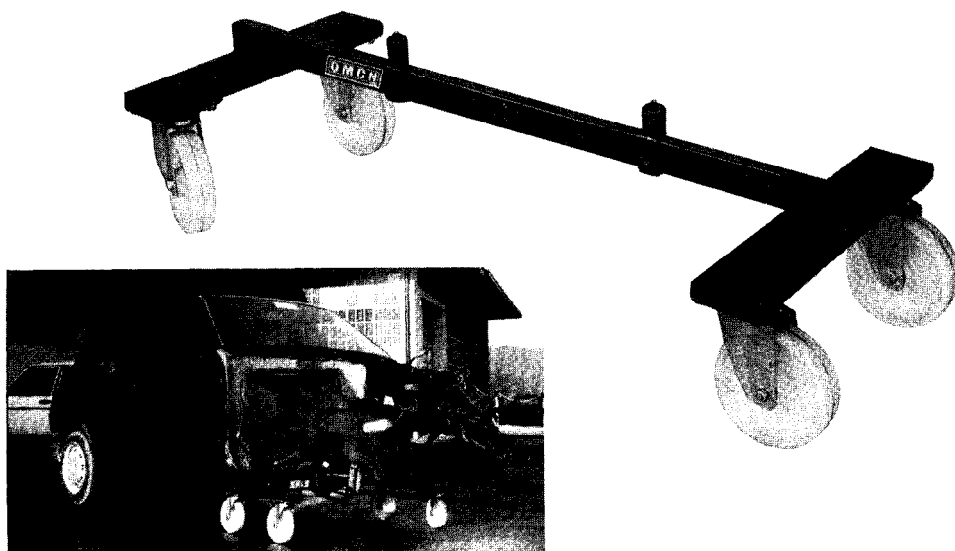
Carro auxiliar, fabricado por ROGEN, para el traslado de una carrocería en situación de reparación.
